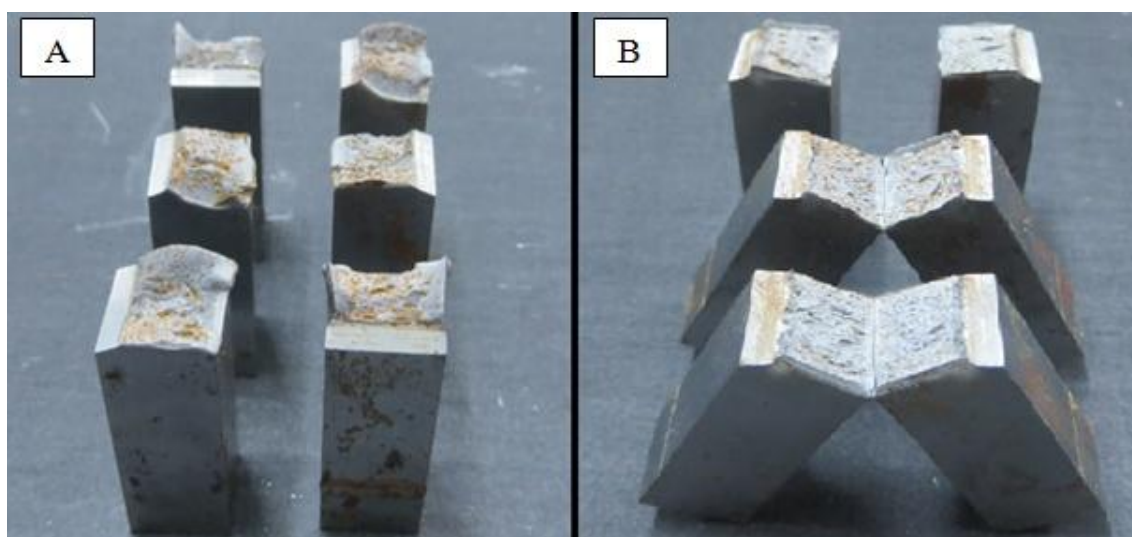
Ensaio de impacto - Superfície da fractura nos provetes soldados pelo fio
